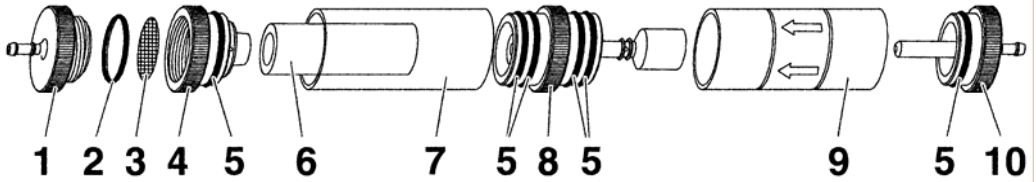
Система подготовки газа – Патрон для сбора конденсата
